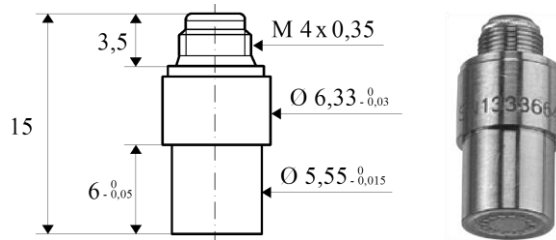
Dimensões do transdutor de pressão retirado do catálogo do fabricante.
